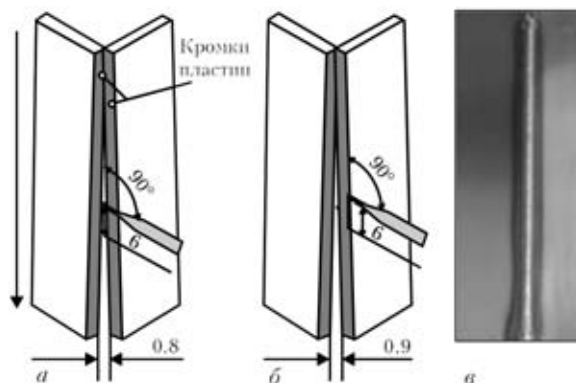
Выполнение обычной МАГ сварки по увеличивающемуся зазору в корне (а, б) и внешний вид соединения (в)
